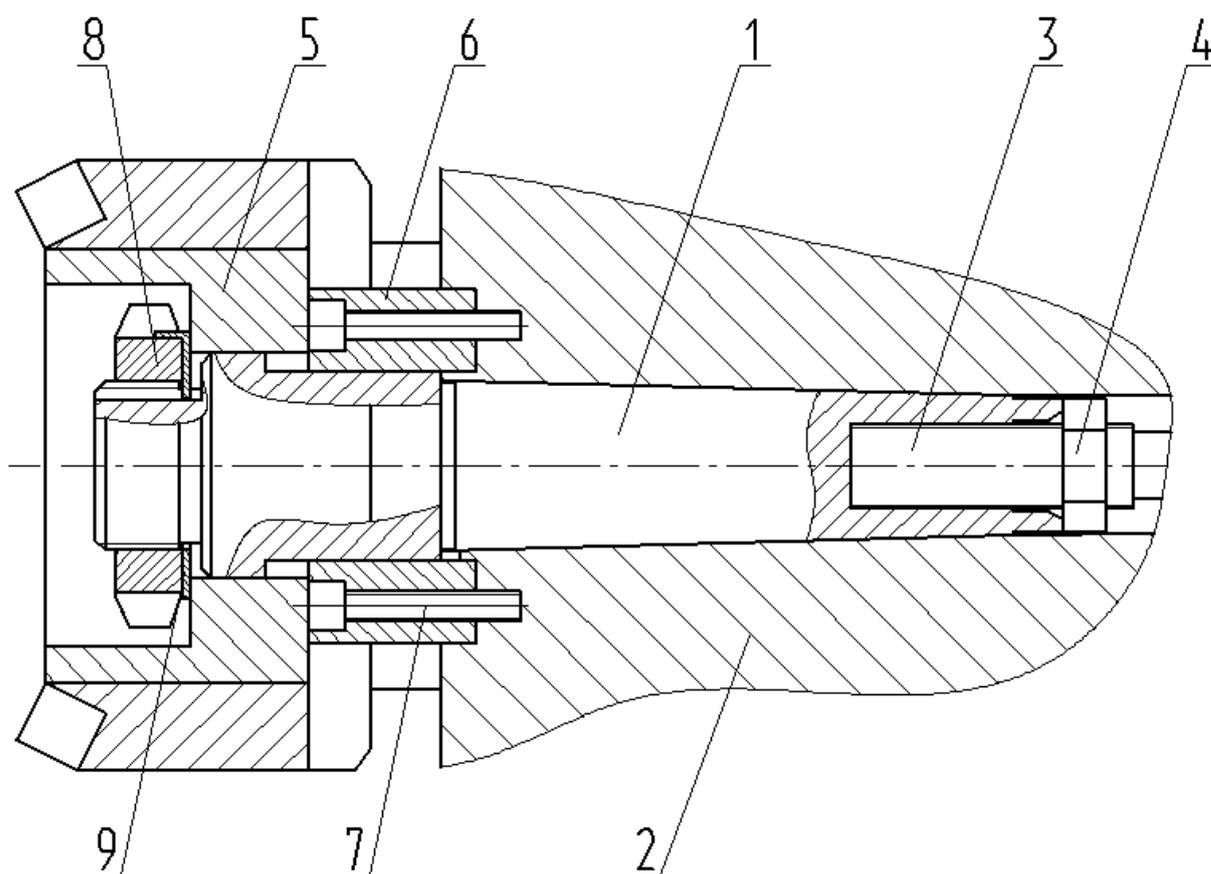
Фрагмент шпиндельного узла фрезерного станка.
